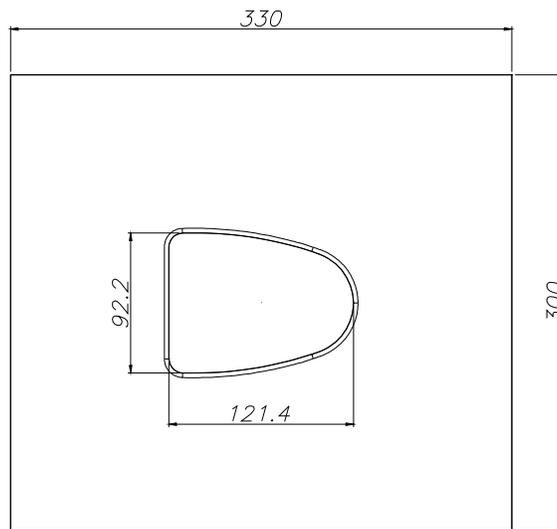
Desenho da matriz com o dimensional da cavidade.
